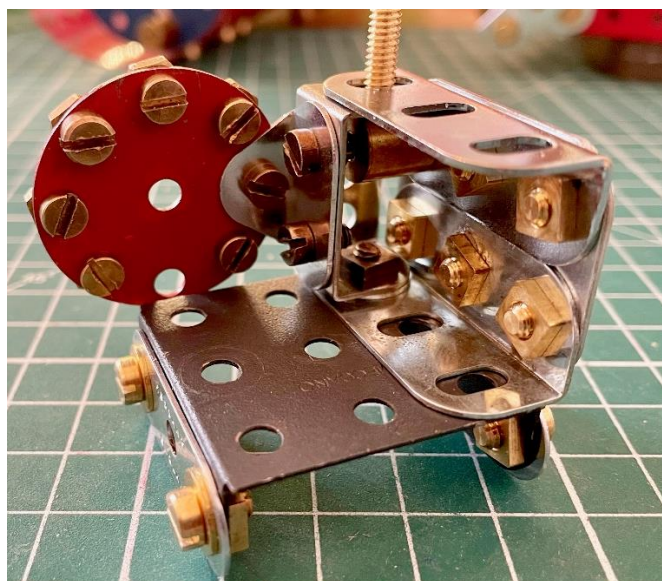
rechts oben im Bild der Threaded Boss mit Schraube zum Ausrichten
